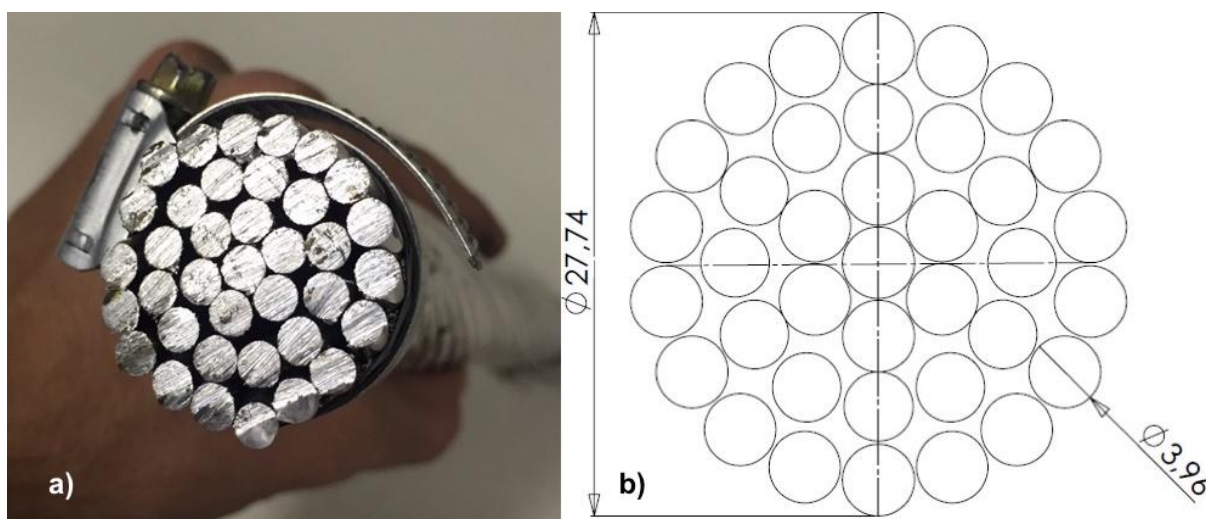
a) Foto da seção transversal do cabo CAL 900, b) Desenho esquemático da seção do condutor CAL 900.
